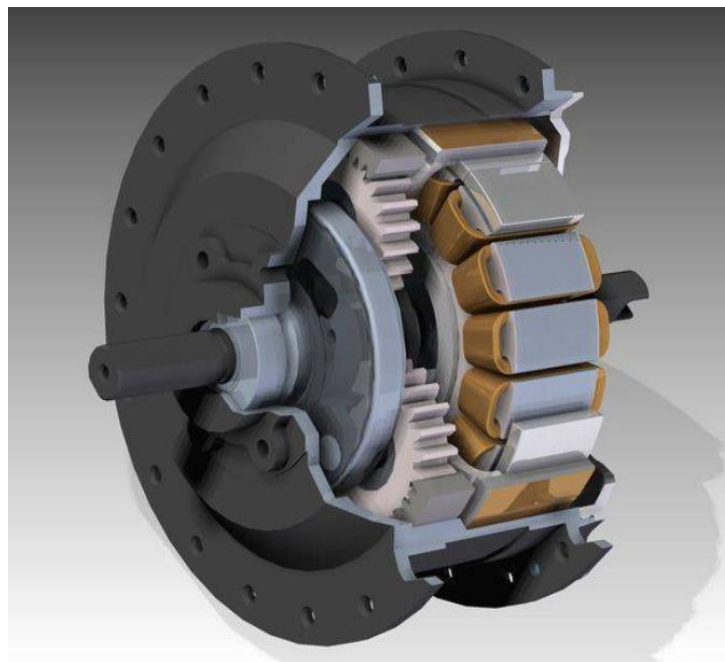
Внутрішня будова редукторного колеса.
